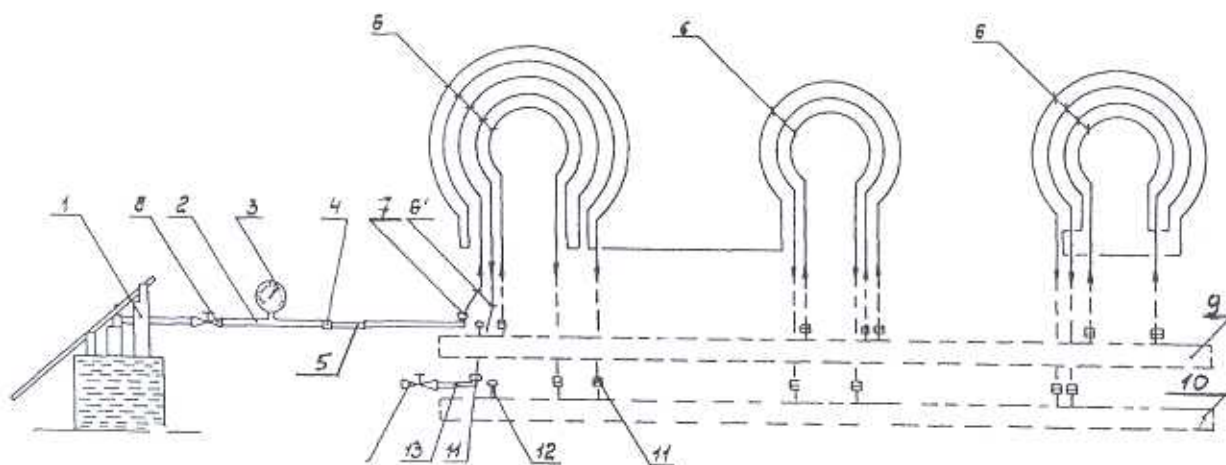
Схема испытаний гидроцепей нажимных колец на герметичность:
